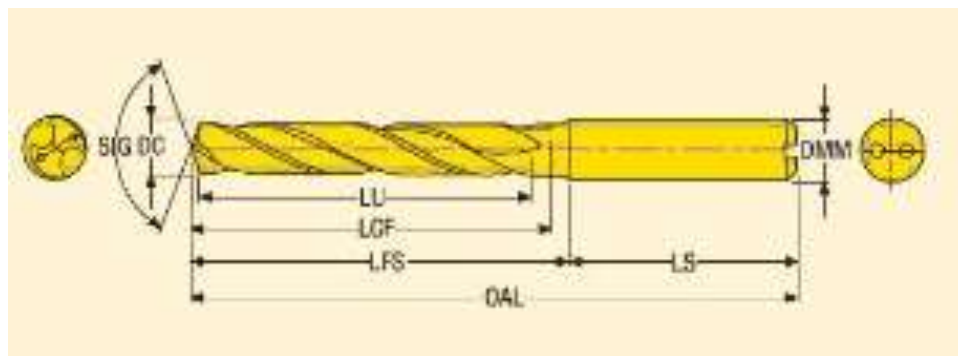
Эскиз сверла SD1105A-0680-043-08R1
